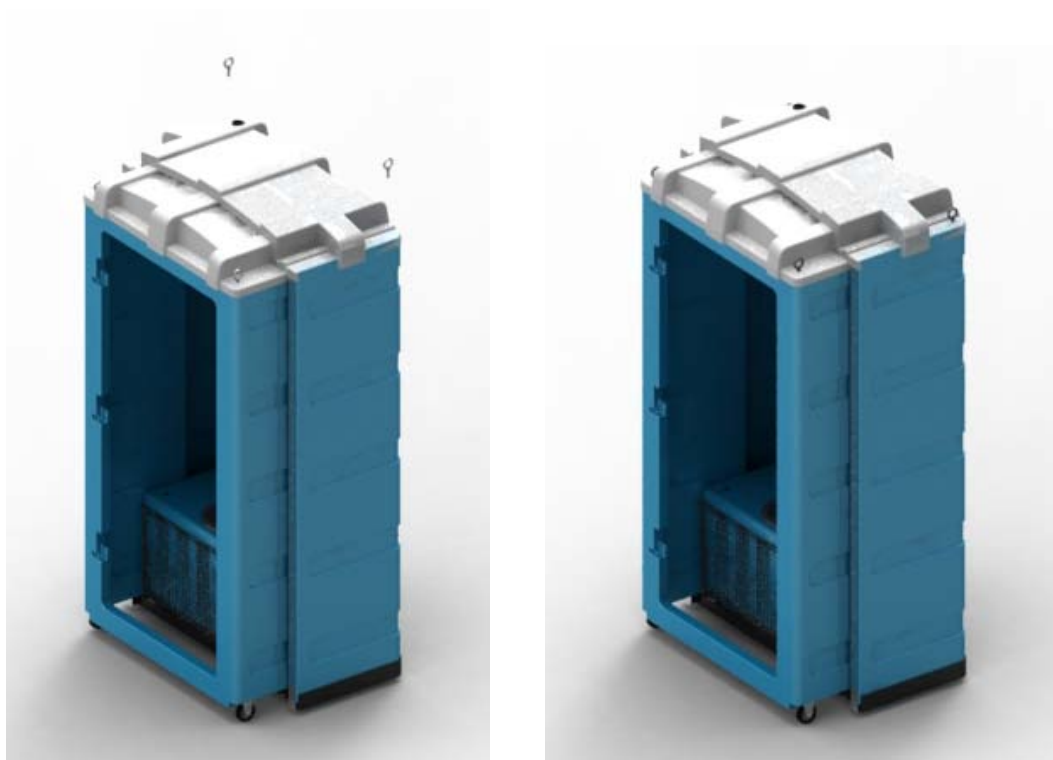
Assemblaggio del kit di sollevamento posteriore
